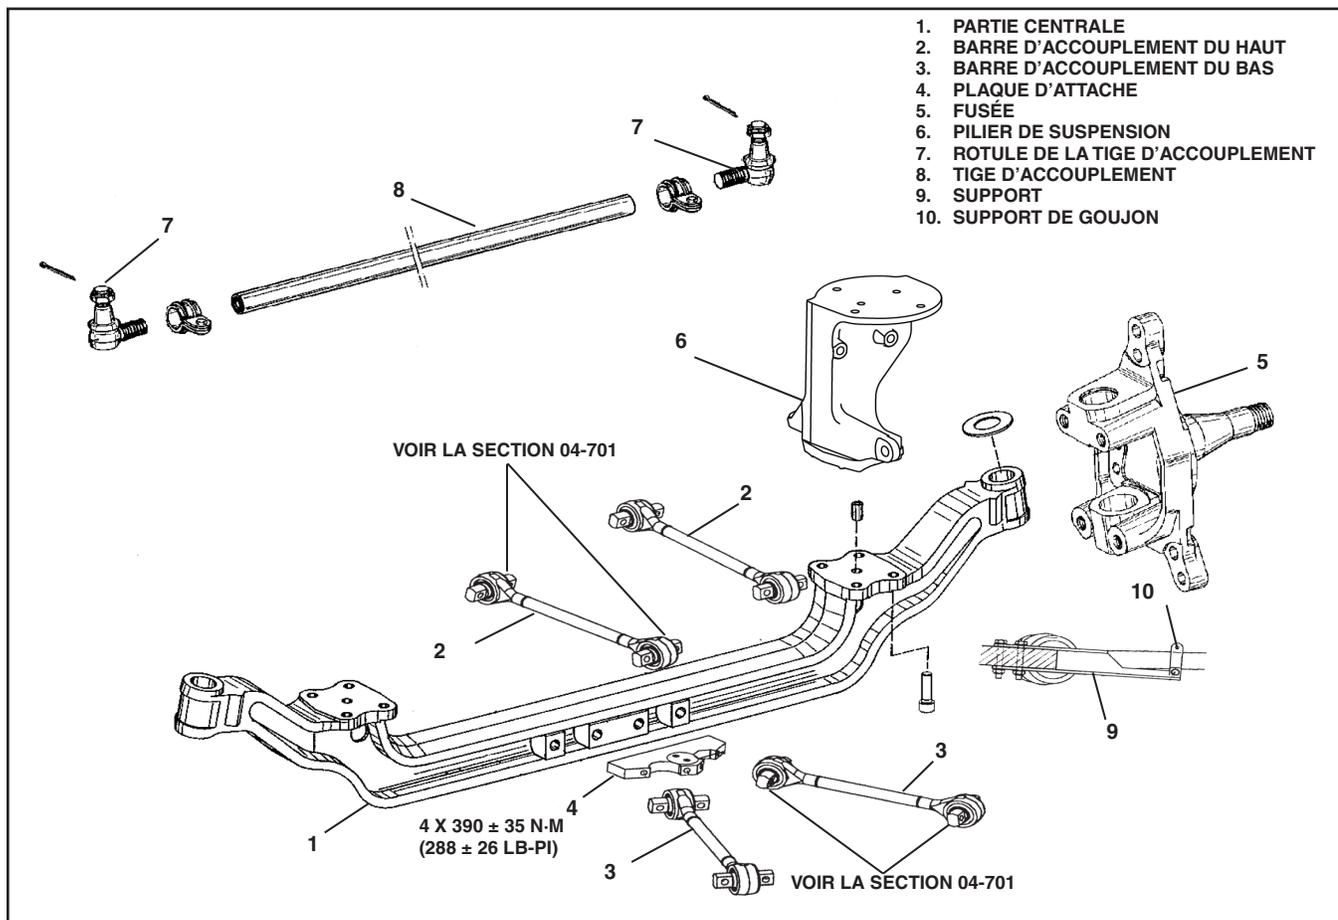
Essieu avant ZF RL-85 A.C, vue explosé (typique)
